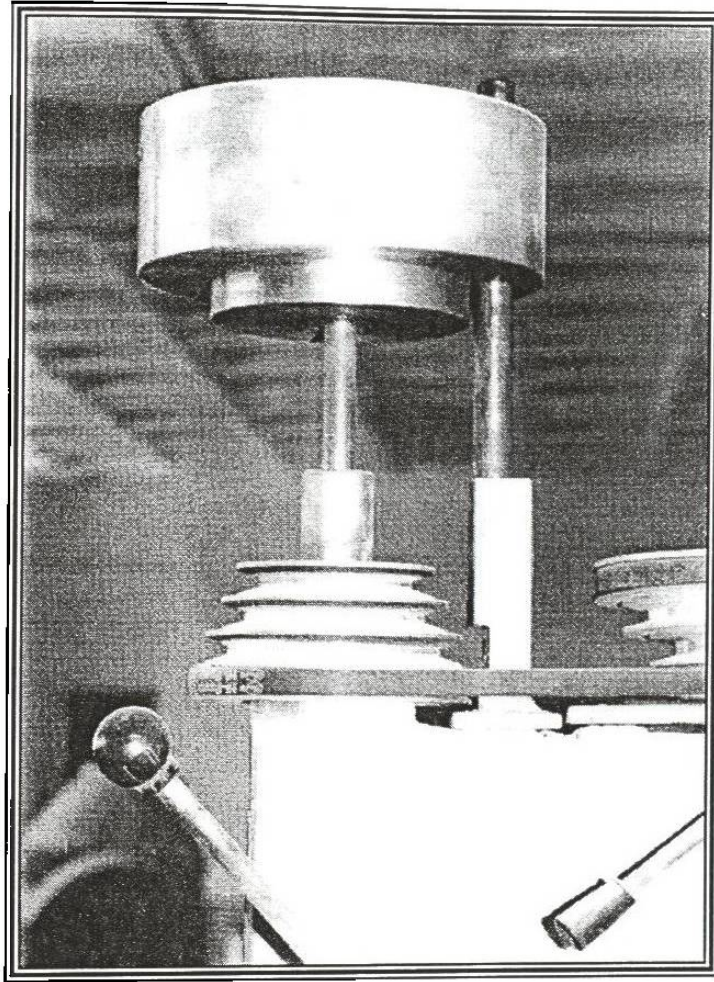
Moldes y equipo para la fabricación de especímenes.
